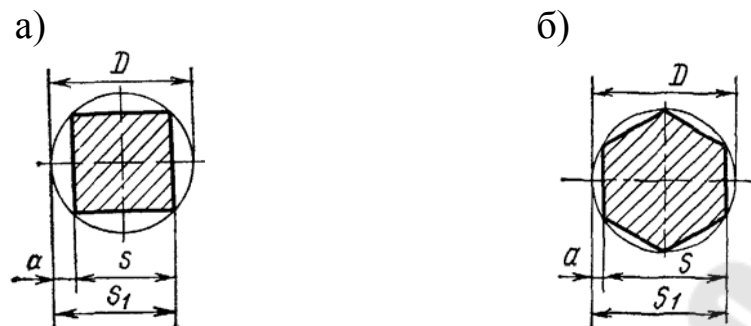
Схема получения многогранника из круглой заготовки:
